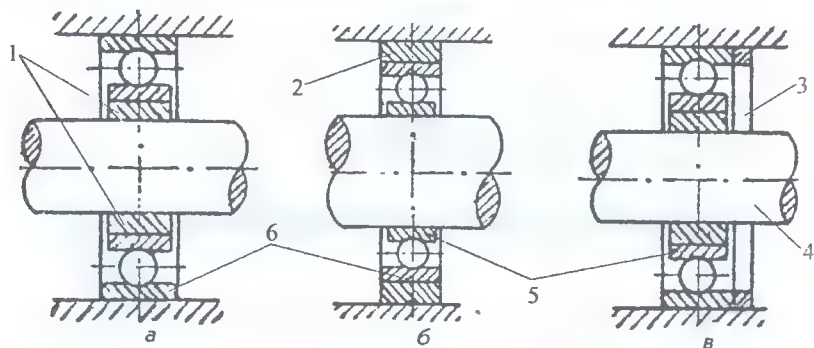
Установка подшипников-заменителей с внутренней (а), наружной (б) ремонтной втулкой; с упорной шайбой (в)
